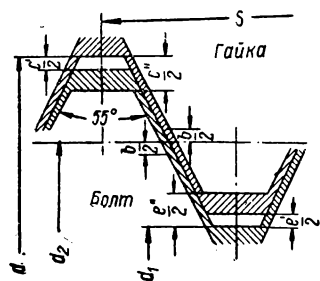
Схема расположения полей допусков дюймовой резьбы.
